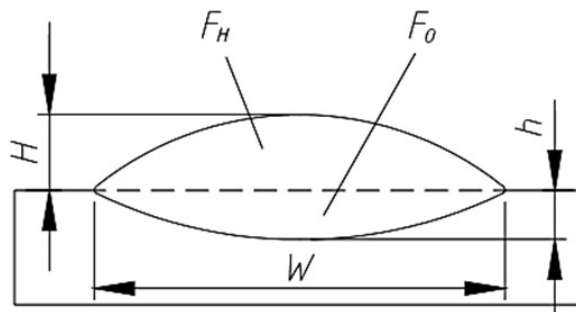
Геометрические параметры наплавленного валика: F_O - площадь подплавленного основного металла; F_H – площадь наплавленного металла; H – высота наплавленного слоя; h – глубина подплавления; W – ширина наплавленного слоя
